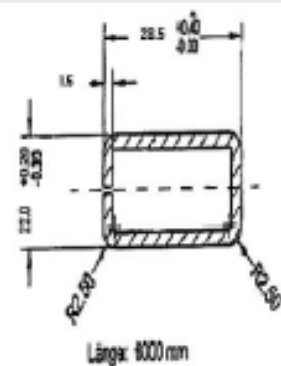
Planșe în secțiune transversală a profilelor montantului ranforsate cu oțel (Cat. nr. 874451)
